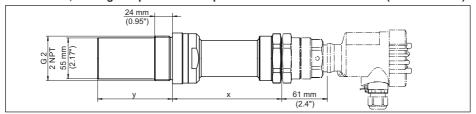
Montageadapter mit Tubus (optional) für frontbündige Montage, für VEGAMIP 61 mit innenliegender Hornantenne, Gewindeausführung G1½ mit PTFE-Abdeckung (auch mit 1½ NPT-Gewinde)
